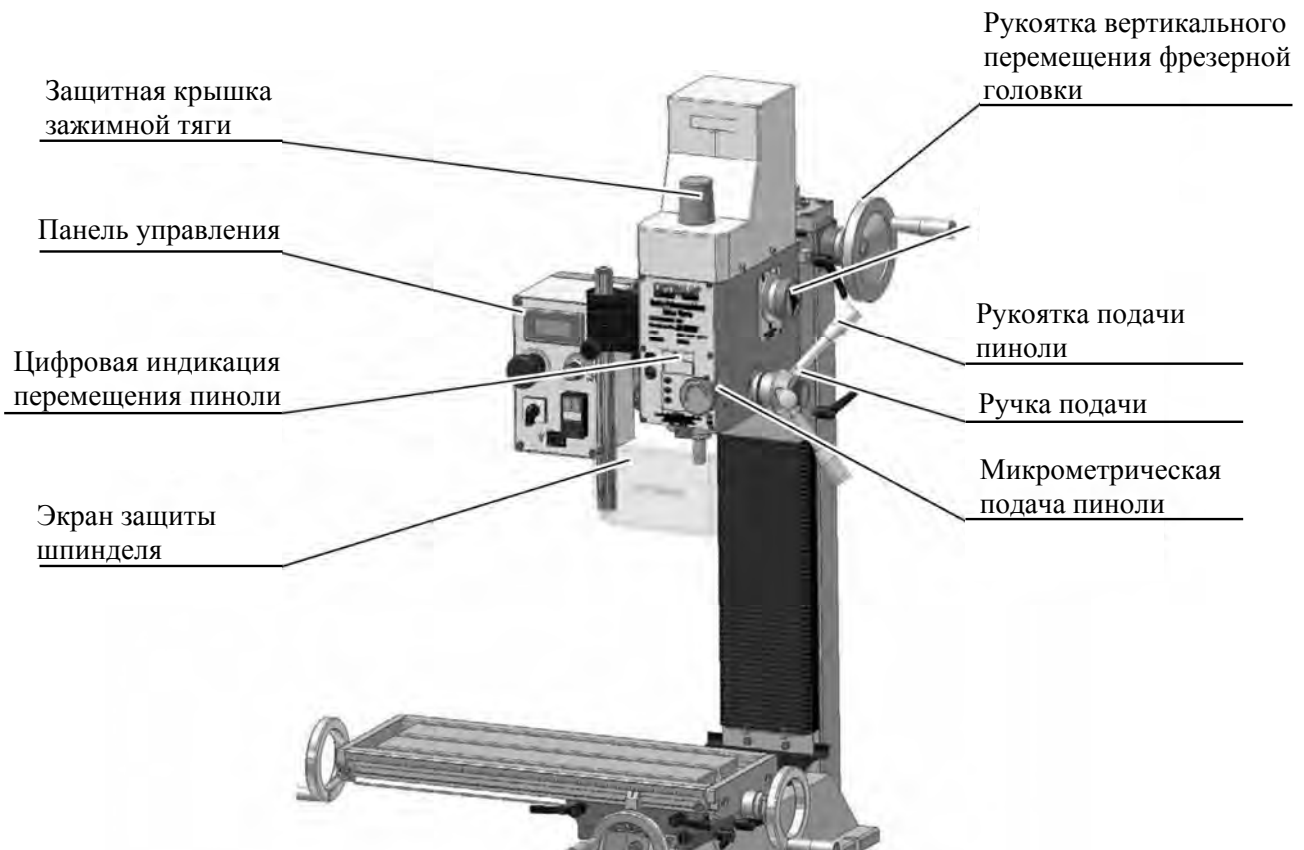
Основные узлы сверлильно-фрезерного станка с ЧПУ Optimill BF 20 Vario
